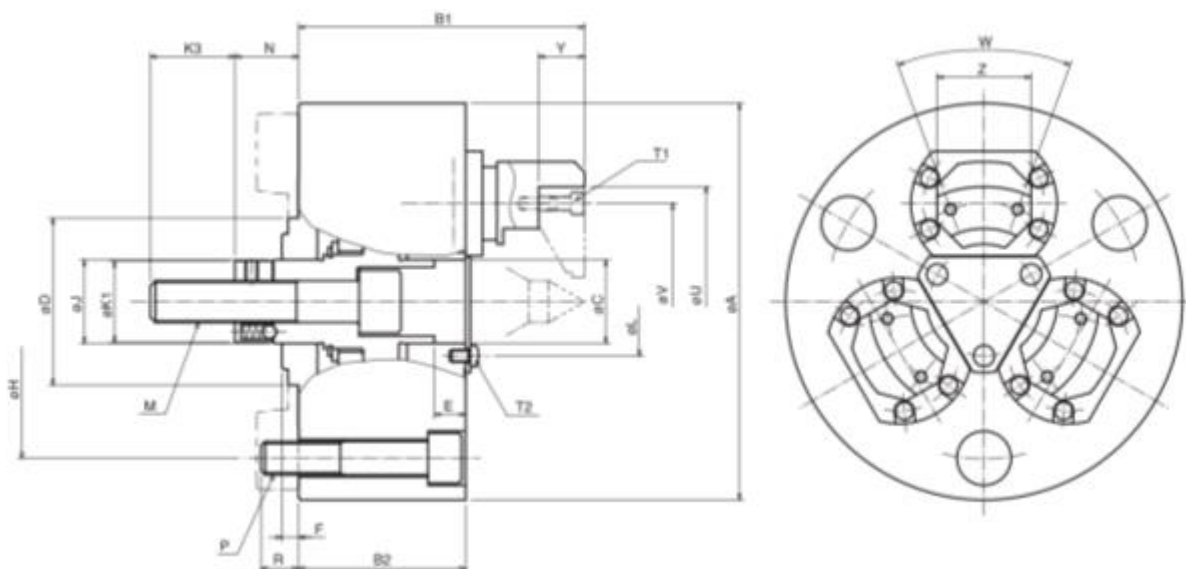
Трёхкулачковый патрон Compensating Chuck СК-51
